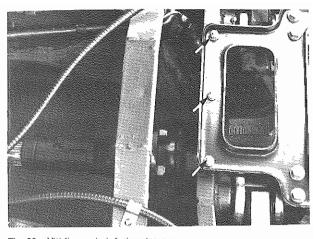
Viti fissaggio inferiore traversa Lower cross member fixing screws
